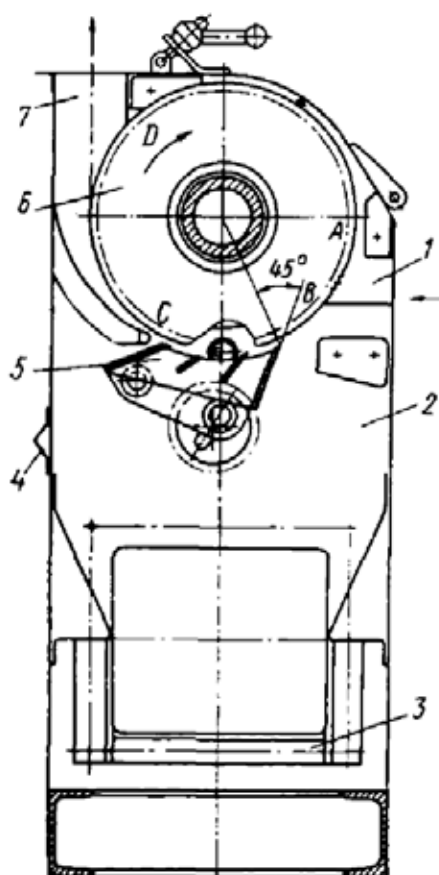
Прямоточная одноступенчатая волоконноочистительная машина ОВПА: 1 — приемная горловина; 2 — угарная камера; 3 — транспортер; 4 — жалюзийное устройства; 5 — колосниковая решетка; 6 — пильный цилиндр; 7 — отводящая горловина.
